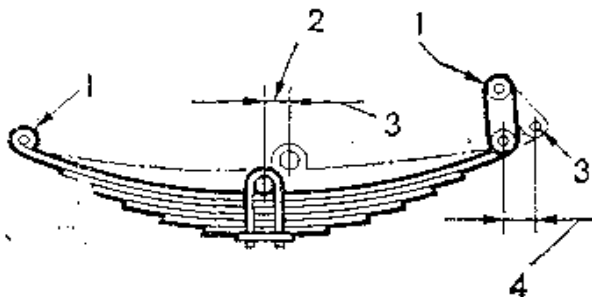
Полуэллиптическая рессора: 1 – кронштейн; 2 – величина перемещения оси автомобиля при сжатии рессоры; 3 – подвижный шарнир серьги; 4 – величина перемещения подвижного шарнира
